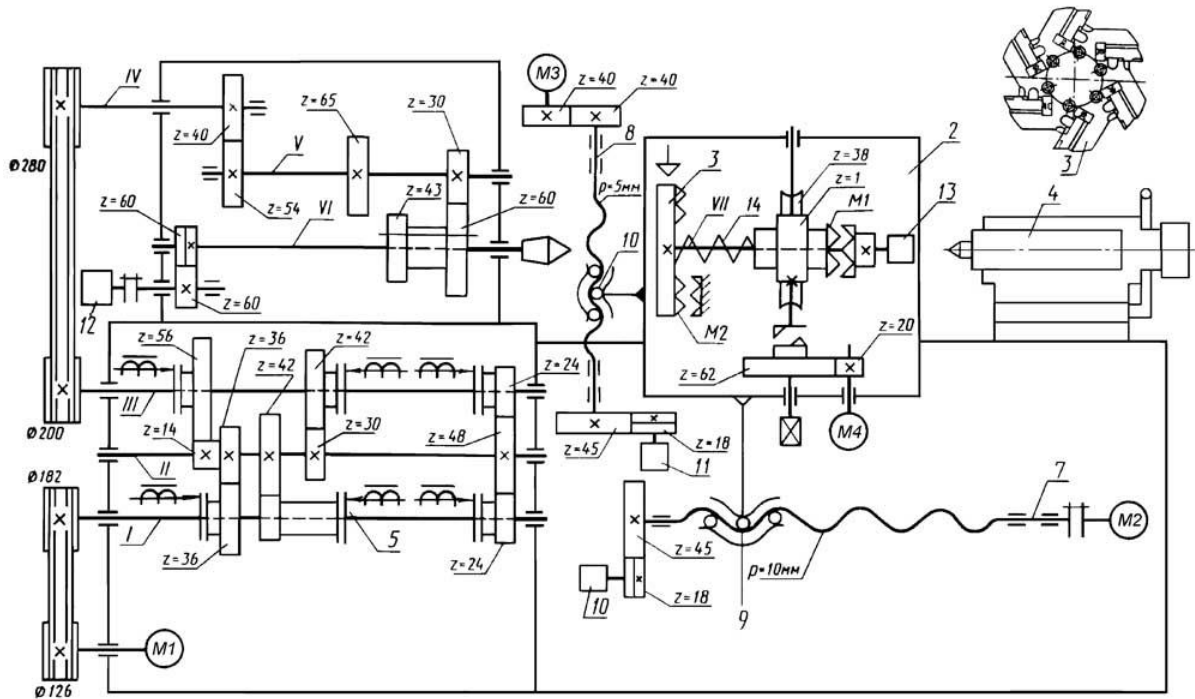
Кінематична схема токарного верстата з ЧПК 16К20Ф3
